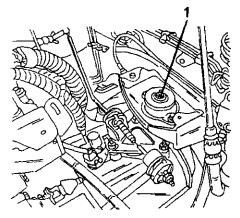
Гайкой (1) левая подвеска двигателя крепится на опоре. Гайна имеет момент затяжки 65 HM.
